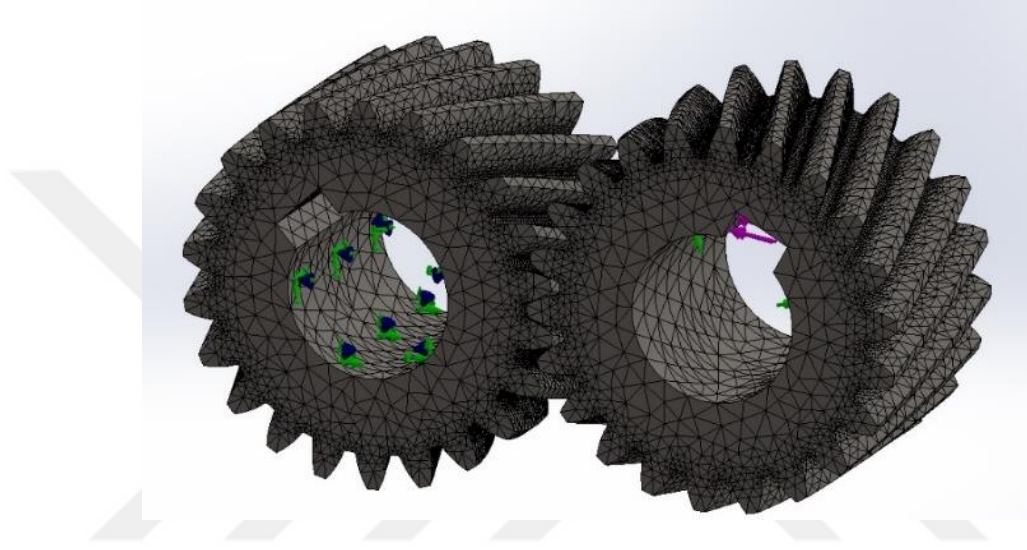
AISI 5115 (A) ve AISI 8620 (B) çelik dişli çarkların eş dişli montajları
